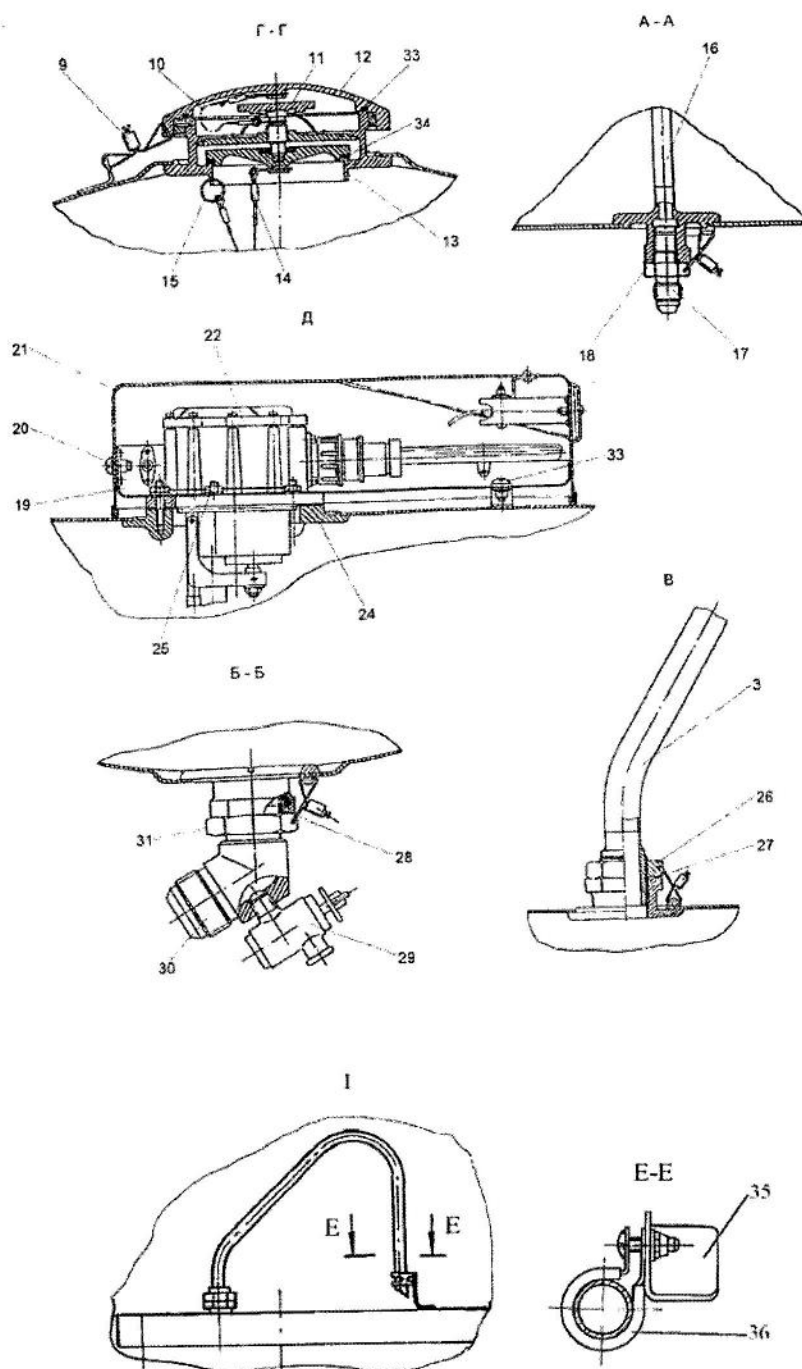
(лист 3 из 3) Дополнительный подвесной топливный бак
